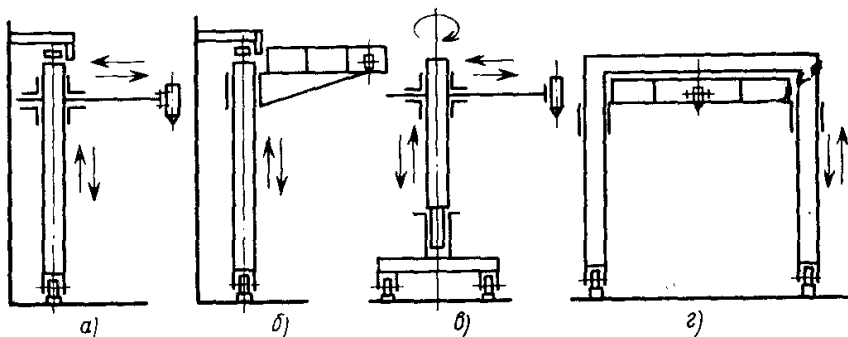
Схемы тележек для сварочных аппаратов:
